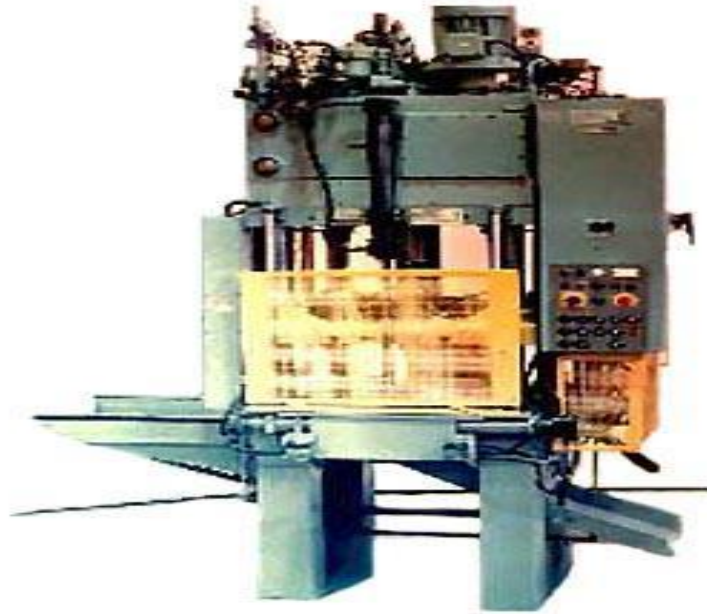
Пресс обрубной П 20А для обрезки литников и облоя
